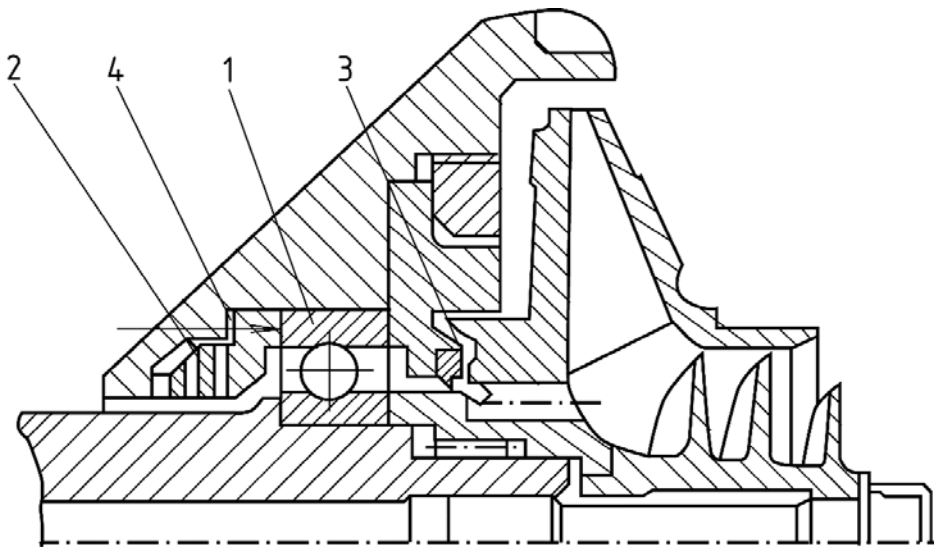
Опора ТНА с предварительным натягом одиночного подшипника:
